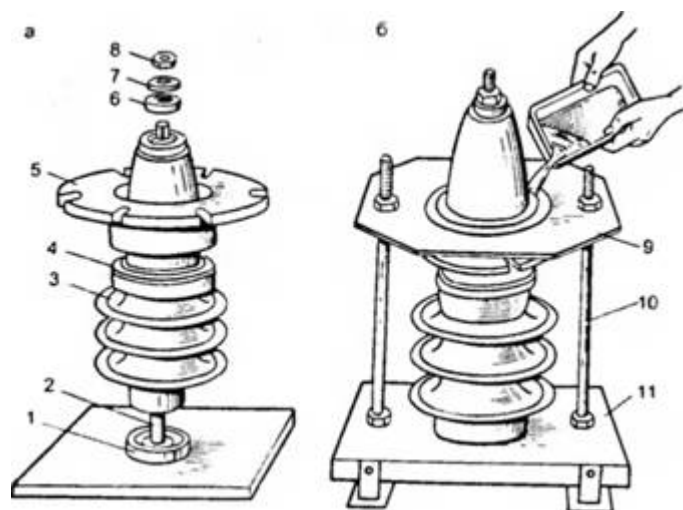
Ремонт ввода трансформатора: а — сборка; б — переармирование; 1 — колпачок; 2 — токопроводящий медный стержень; 3 — фарфоровый изолятор; 4 — резиновая маслостойкая прокладка; 5 — фланец; 6, 7 — гетинаксовая и стальная шайбы; 8 — гайка; 9, 11 — нажимная и опорная плиты; 10 — шпилька
